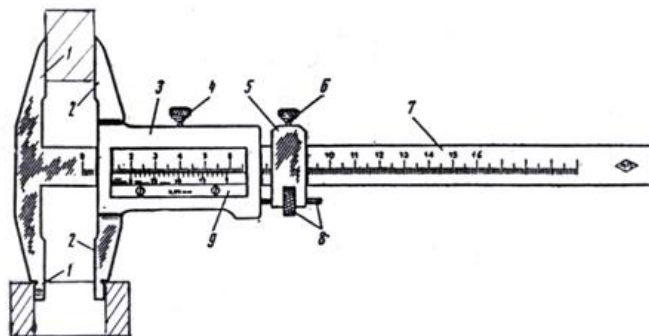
Конструкция штангенциркуля ШЦ – II:
